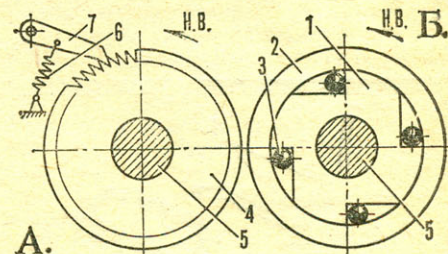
Храповые механизмы (А — зубчатый, Б — роликовый): 1 — втулка, 2 — ведомая втулка, 3 — ролики, 4 — зубчатое колесо, 5 — вал мультипликатора, 6 — пружина, 7 — собачка.
